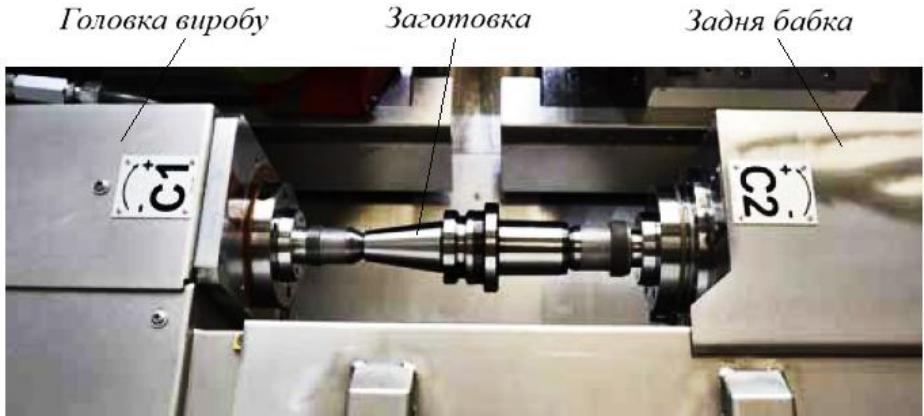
Закріплення заготовка в головці виробу і задній бабці
